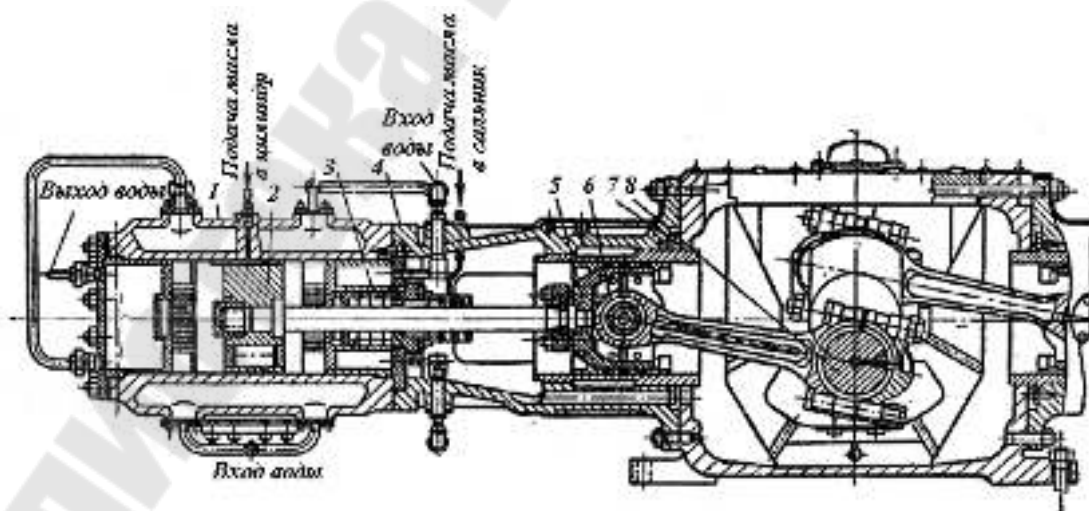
[15]. Горизонтальный аммиачный крейцкопфный оппозитный компрессор АО600: 1 – цилиндр; 2 – поршень; 3 – сальниковое уплотнение штока; 4 – направляющие крейцкопфов; 5 – крейцкопф; 6 – шатун; 7 – рама; 8 – коленчатый вал
